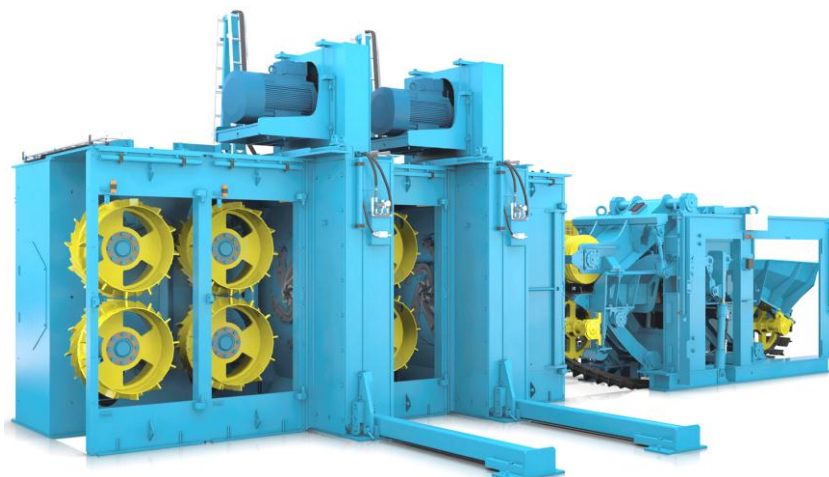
Станок VK8000-Combi-2R с двумя роторными головками
